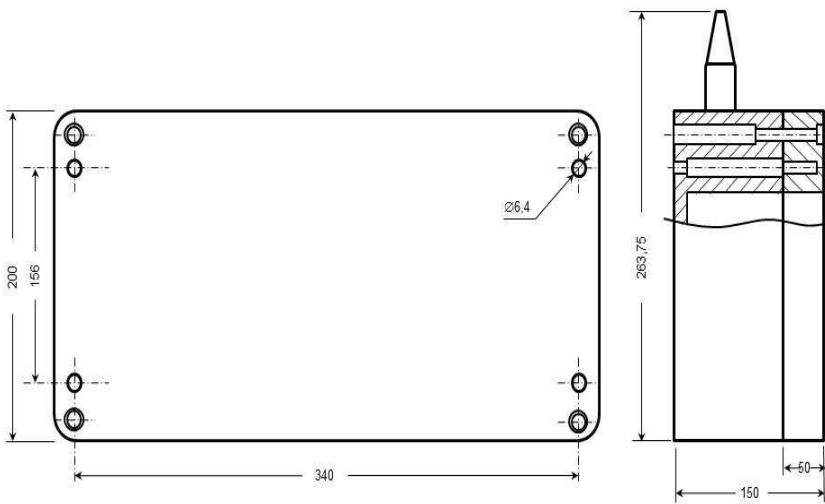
Габаритные и присоединительные размеры ПВ
